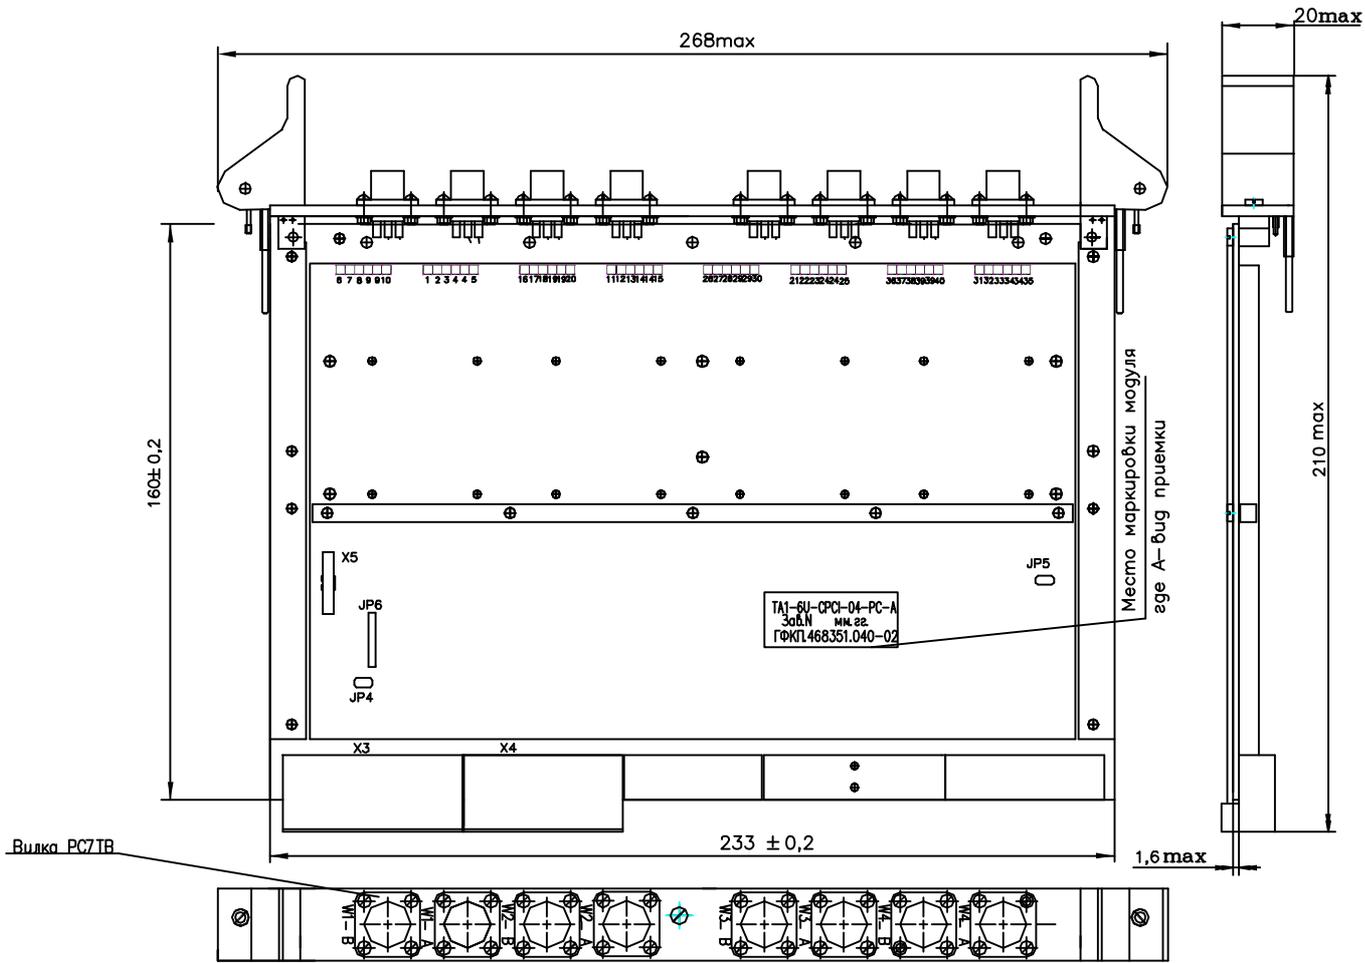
Габаритный чертеж изделия ТА1-6U-СРСІ-04-РС –А
